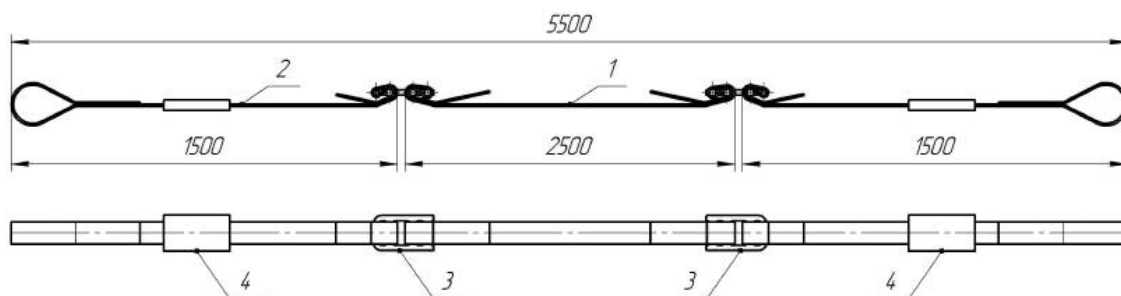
Общий вид крепления МВ КТБ5 7,0/1500-2500
